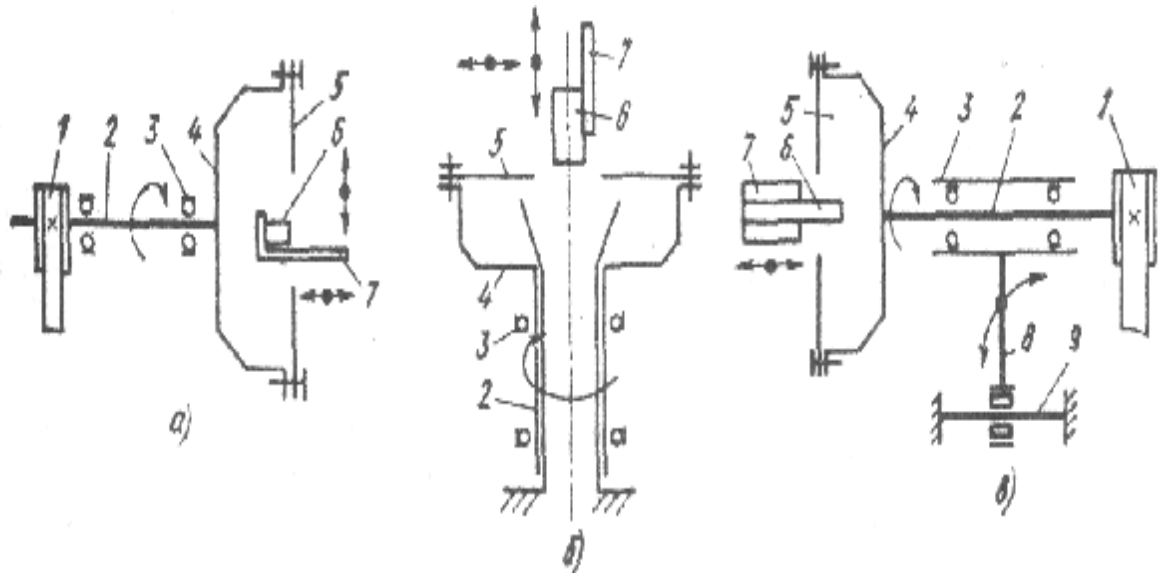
Схемы конструктивных компоновок станков для резки слитков алмазными кругами с внутренней режущей кромкой:
